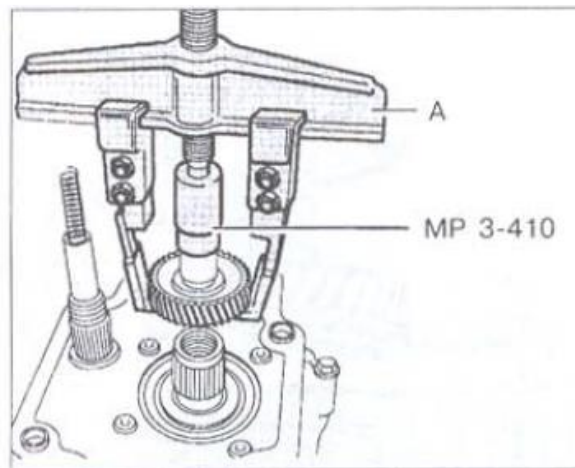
Знімання шестерні п'ятої передачі
